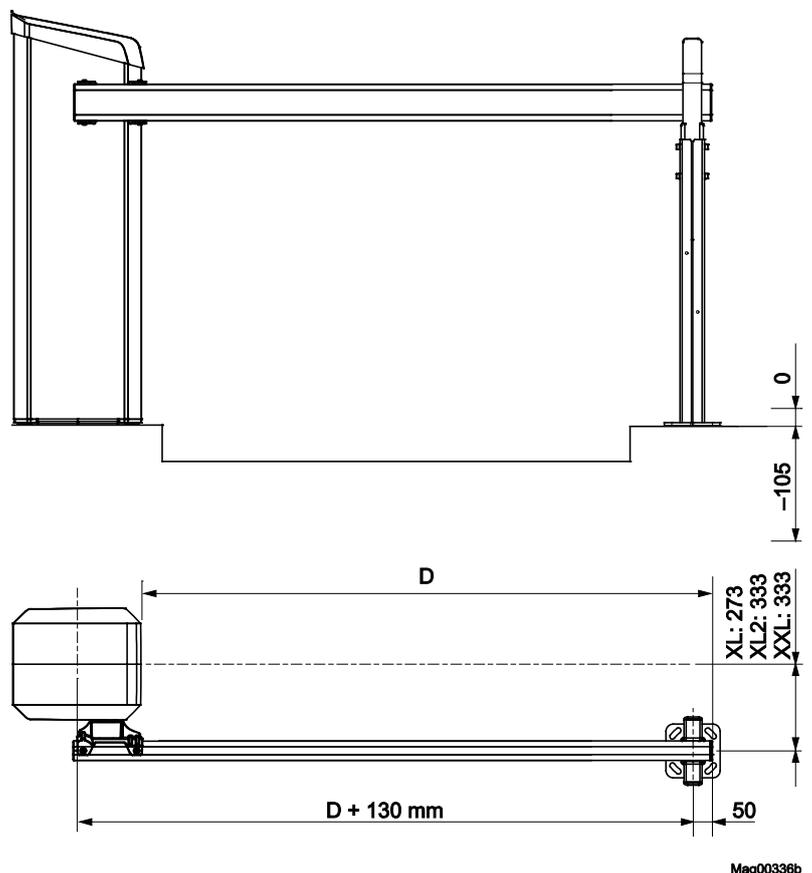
Abmessungen Schrankengehäuse – Pfosten (Maße in mm)
